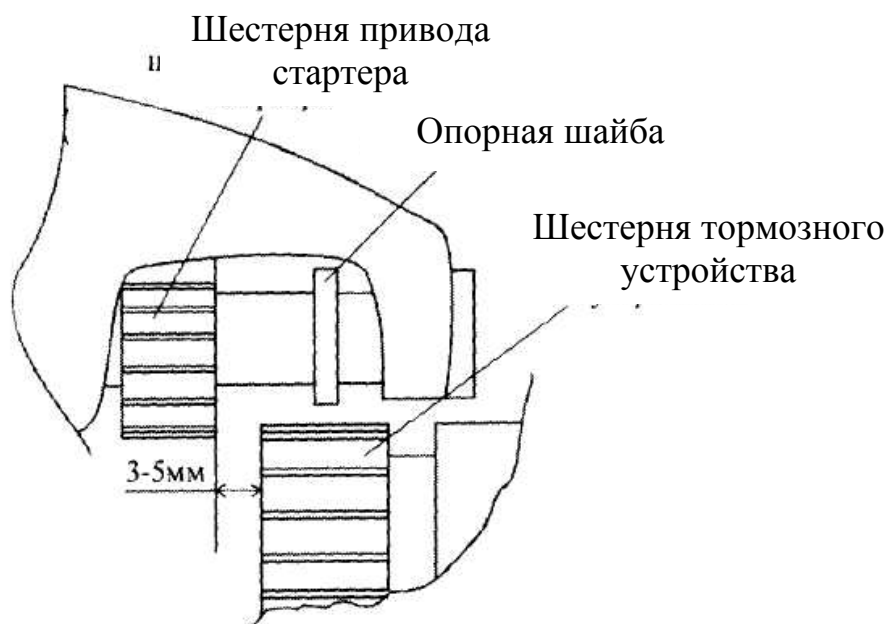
Соответствие положений шестерни привода стартера и шестерни тормозного устройства стенда
